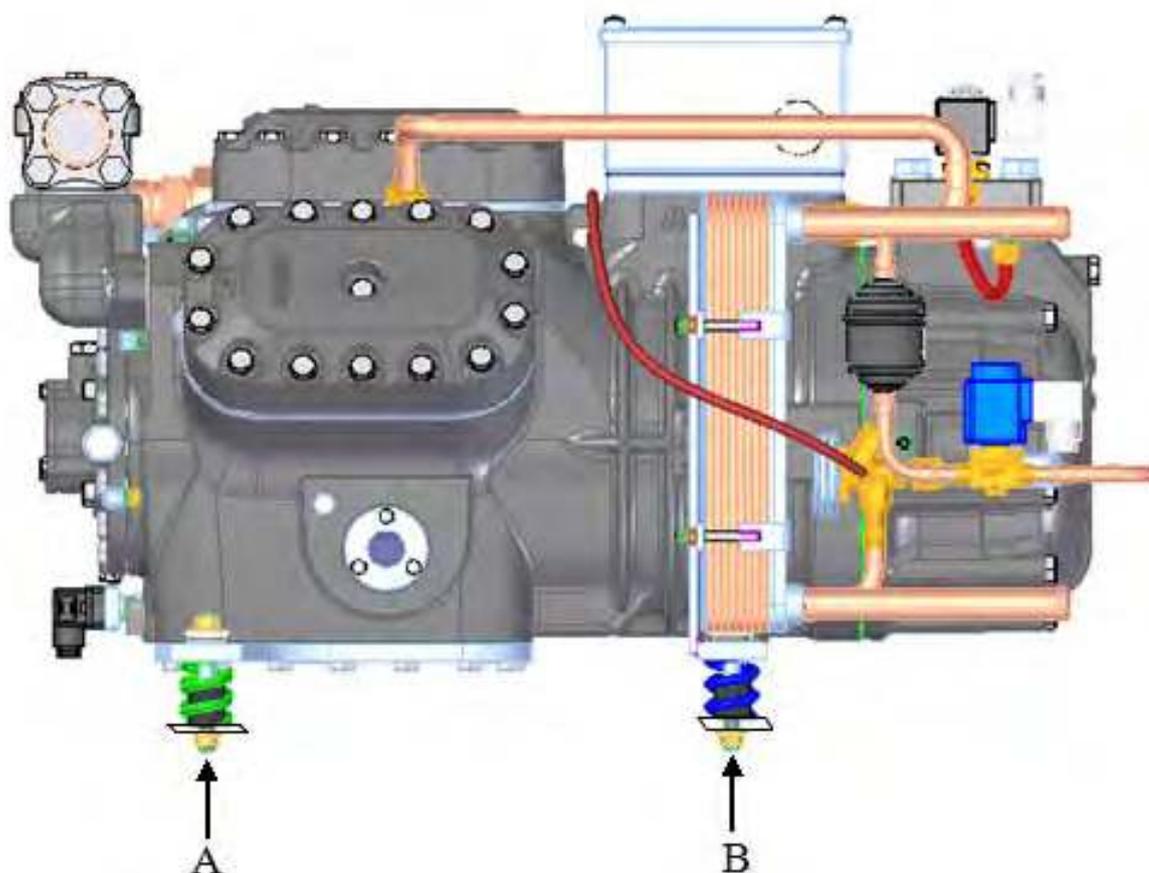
Положение сборки пружинного амортизатора компрессора серии SBC
